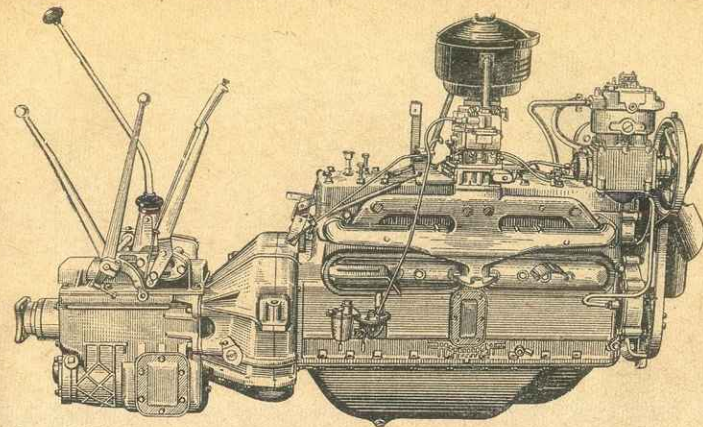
Двигатель со сцеплением и с коробкой передач (вид справа)
